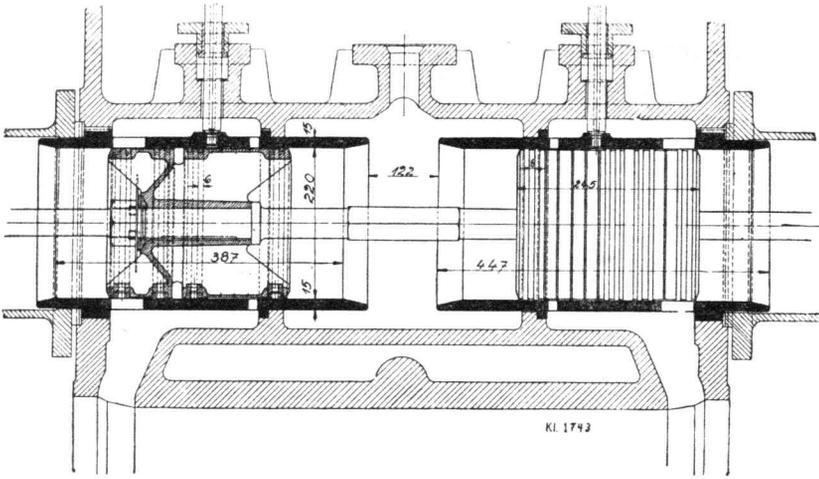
Kolbenschieber, Bauart Schichau, für 220 mm Durchmesser mit schmalen Federringen und doppelter innerer Einströmung.
